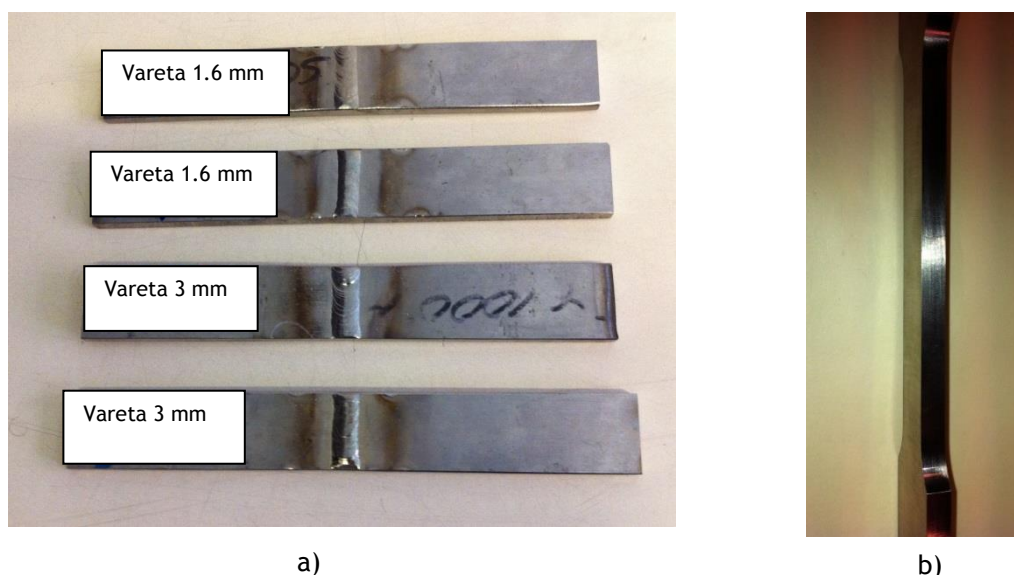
Provetes para caracterização da junta soldada por TIG: a) após soldadura; b) após maquinagem
